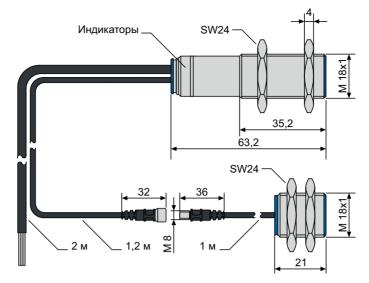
Габаритные размеры датчиков dbk+4/...
